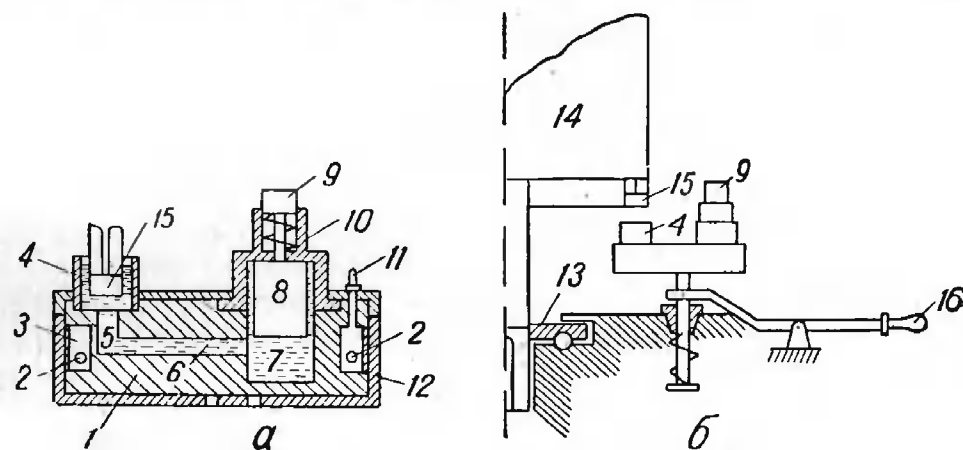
Паяльник для пайки стержней ротора: а — разрез паяльника; б — установка для пайки.
